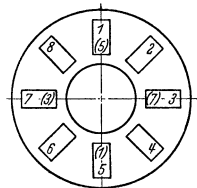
Umlegen der Werkstücke in Läppmaschinen.
